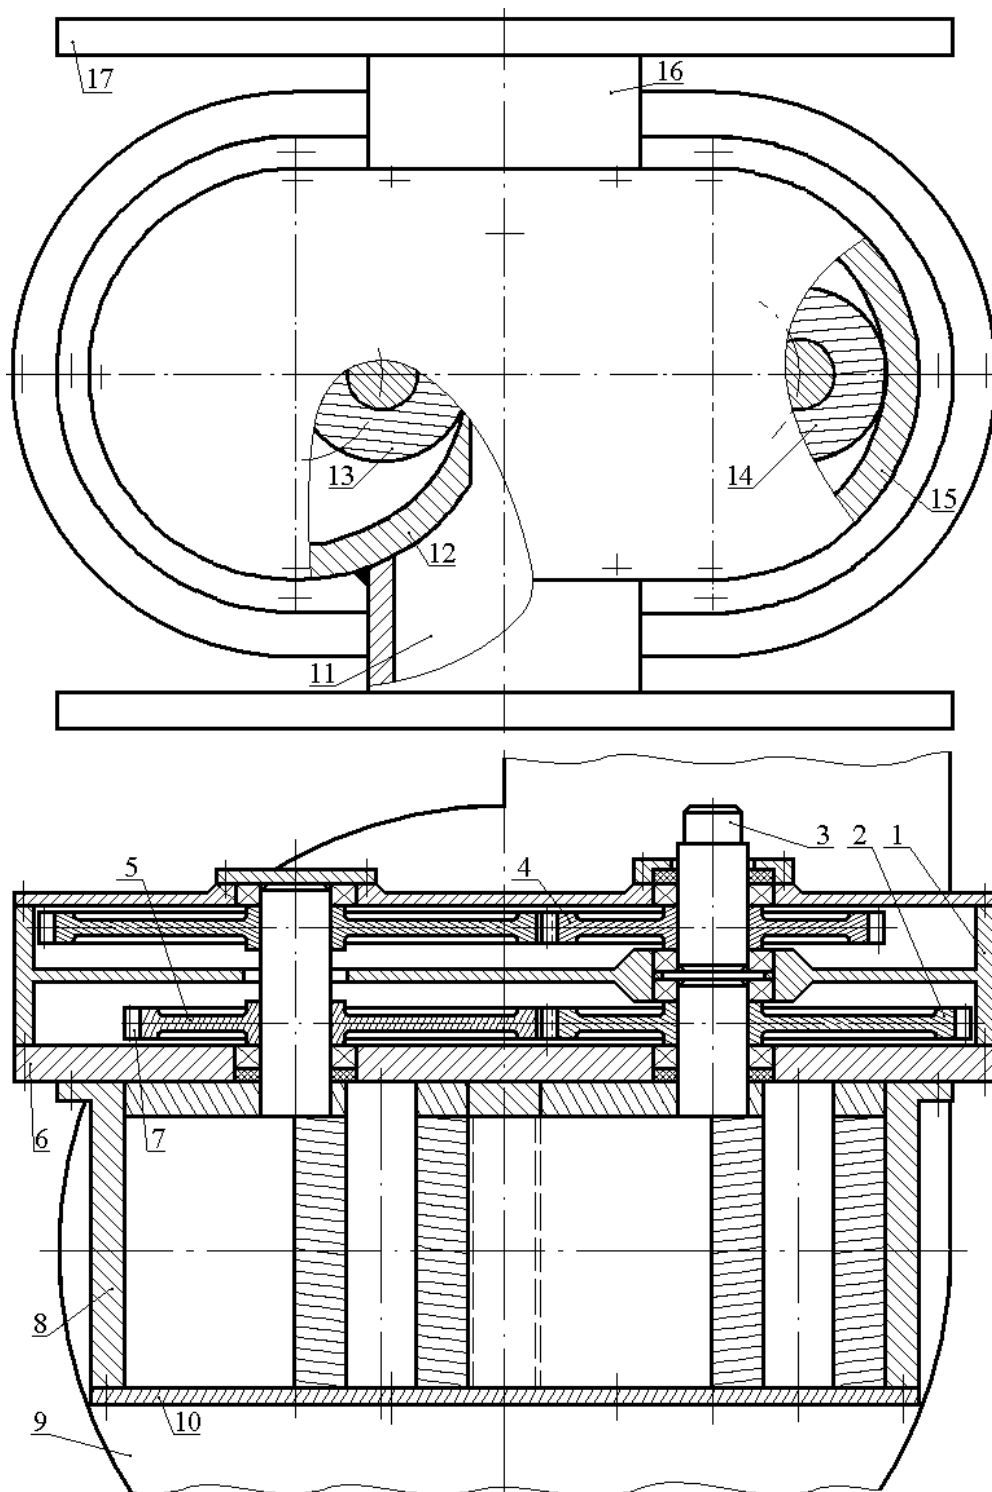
Разрабатываемая ГМОВ с дополнительным редуктором
